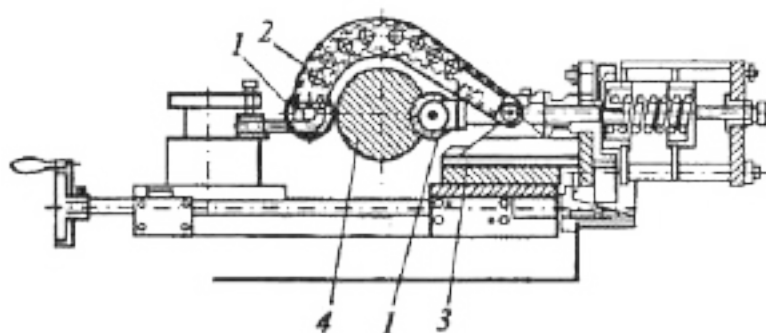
Двороликове пневматичне обкатне пристосування: 1 — обкатні ролики; 2 — скоба; 3 — головка; 4 — деталь
